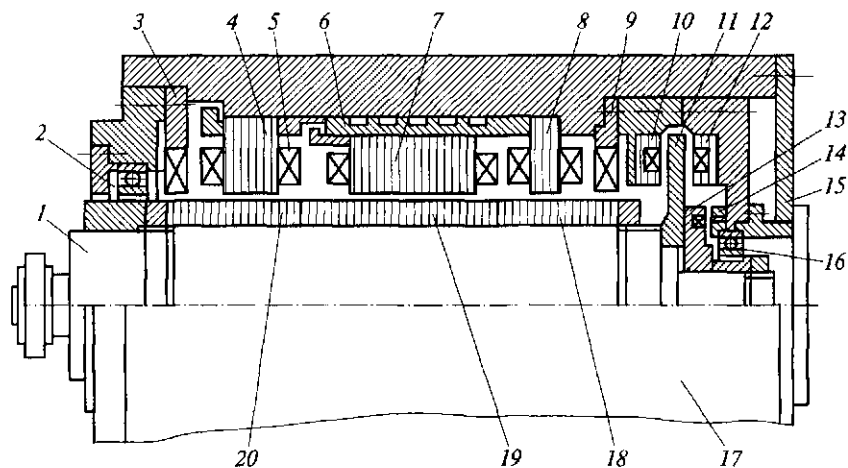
Шпиндельный узел с активными электромагнитными опорами: 1 — вал; 2 — воздушное уплотнение; 3, 9 — индуктивные датчики; 4 — пакет чистой стали; 5 — обмотка электромагнита; 6 — рубашка охлаждения; 7 — статор; 8, 18 — соответственно статорная и роторная части задней опоры; 10, 12 — кольцевые электромагниты; 11 — диск; 13 — мерительное кольцо; 14 — статорная часть индуктивного датчика; 15 — фланец; 16 — резервная опора; 17 — корпус; 19 — ротор; 20 — роторная часть неподвижной передней опоры
